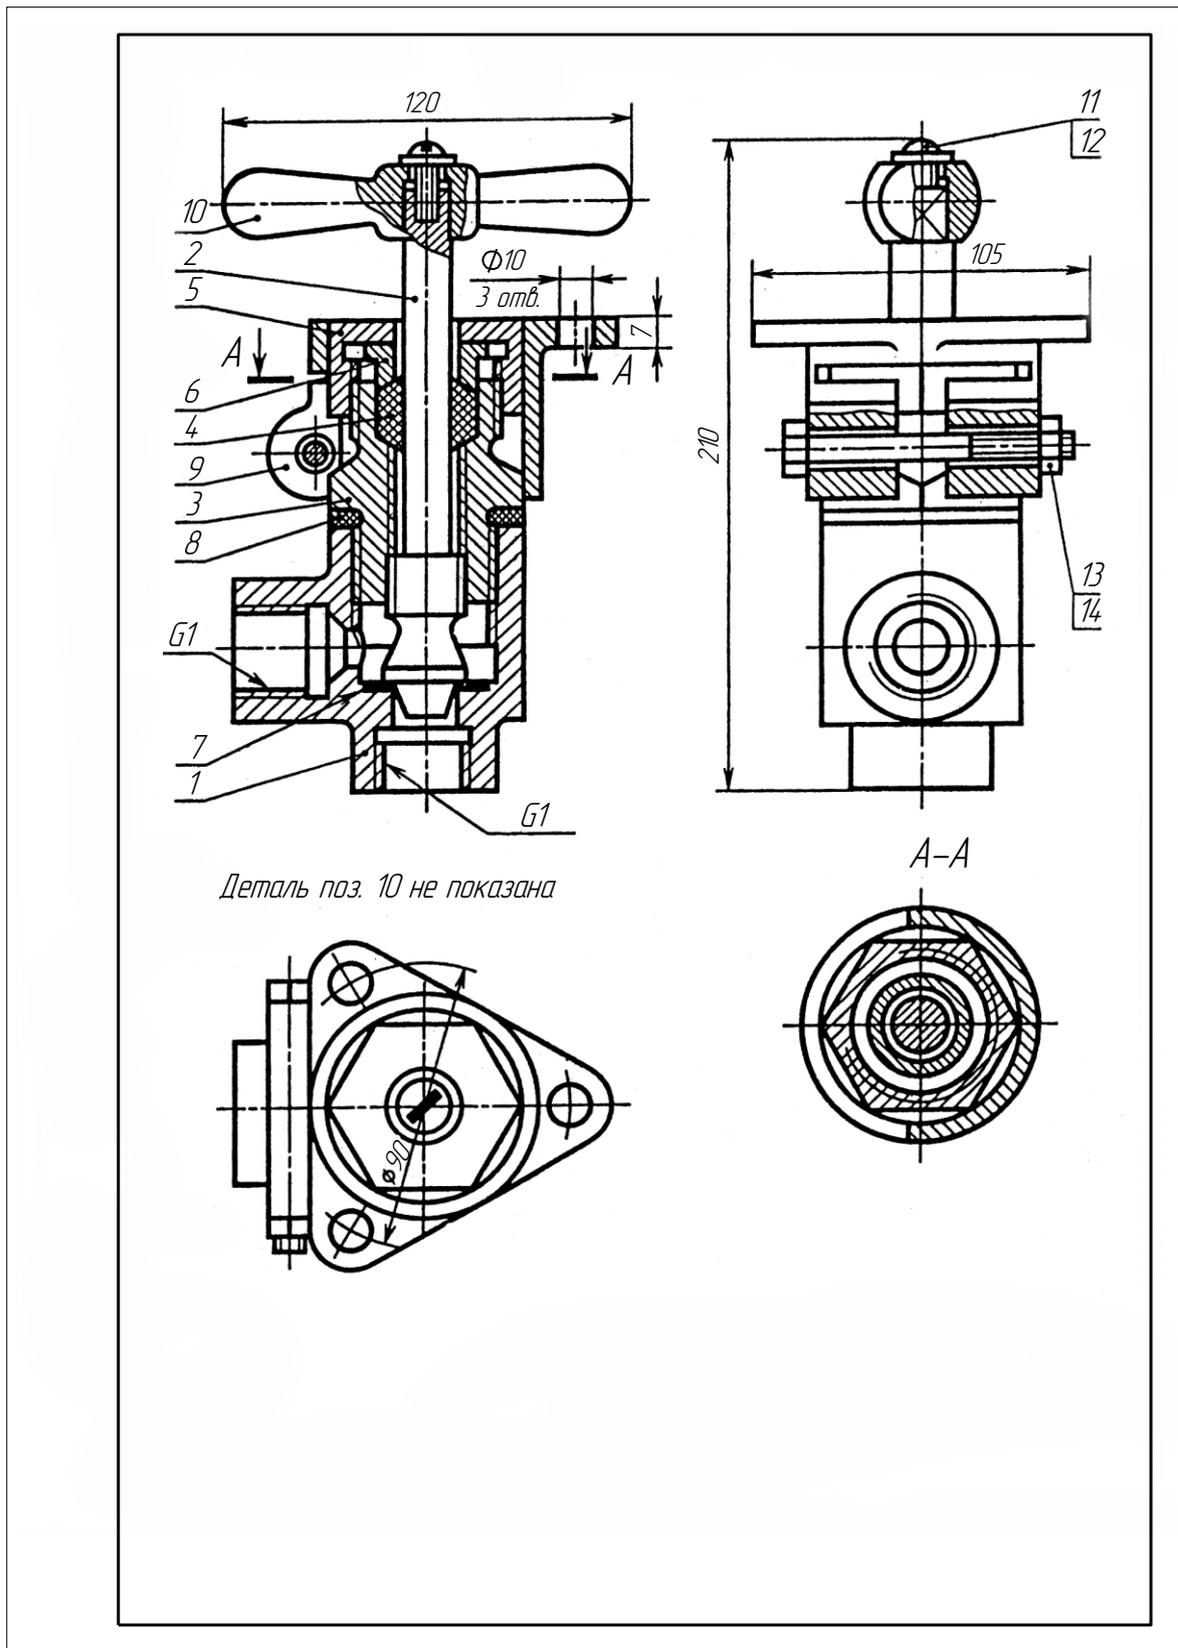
Вентиль угловой запорный сальниковый муфтовый:
